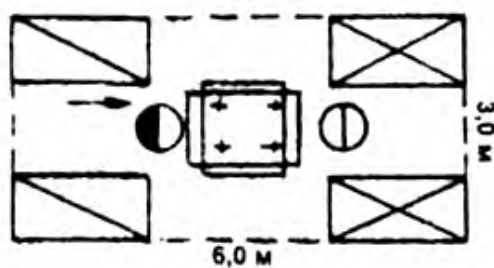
Условное обозначение торцовочного станка ЦПА-40
